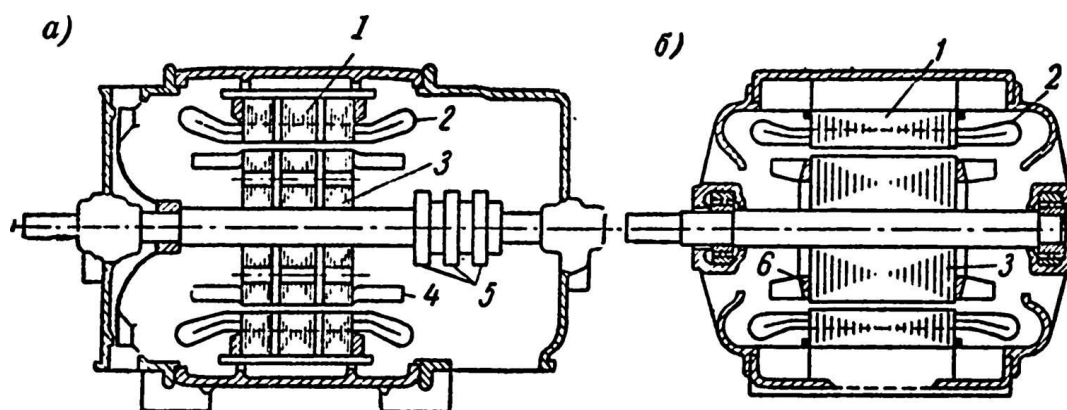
Конструктивная схема трехфазного асинхронного двигателя: а — с фазной обмоткой ротора, б — с короткозамкнутой обмоткой ротора
